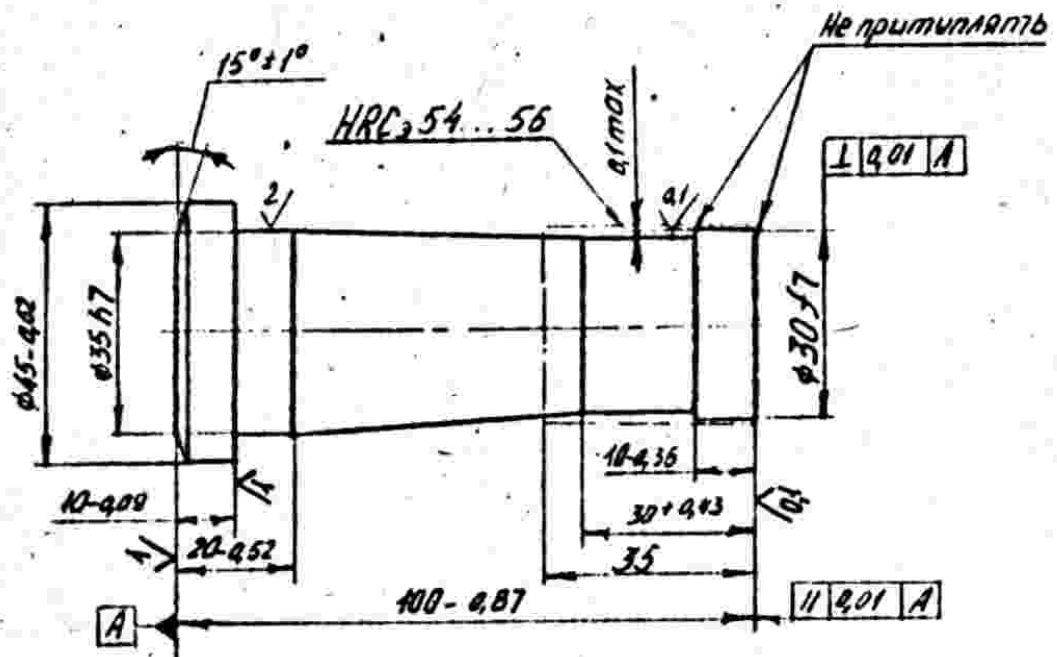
Конструкция пуансона цилиндрической формы без стержня
